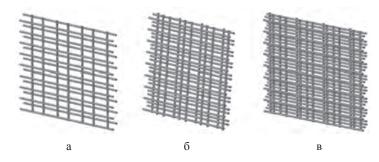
Сетка-заготовка для изготовления пулерассеивающих противоосколочных панелей сварных
